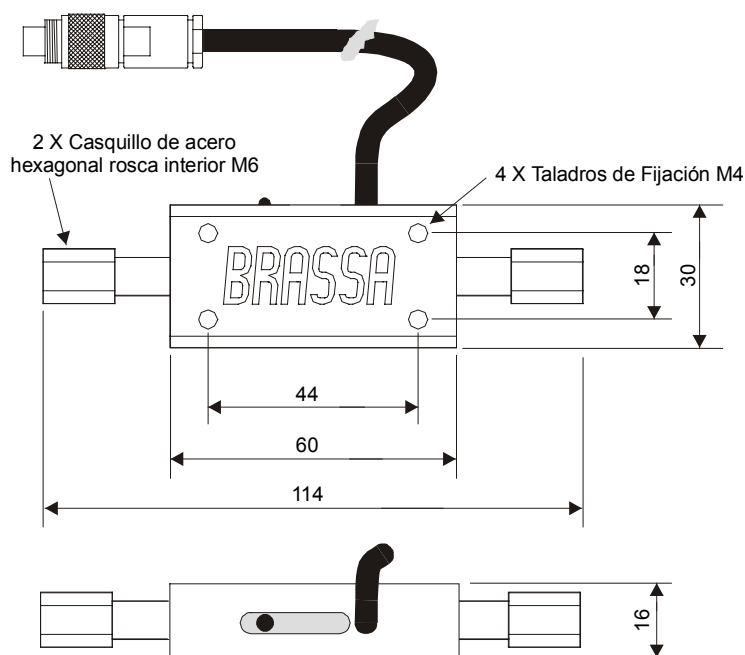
Dimensiones Captador de Posición CSEM-C-01
